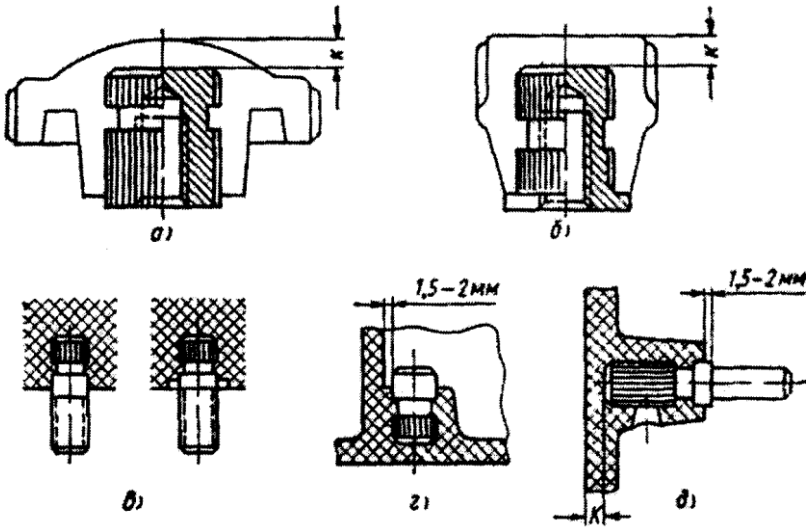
Варіанти конструкцій деталей з пластмас
